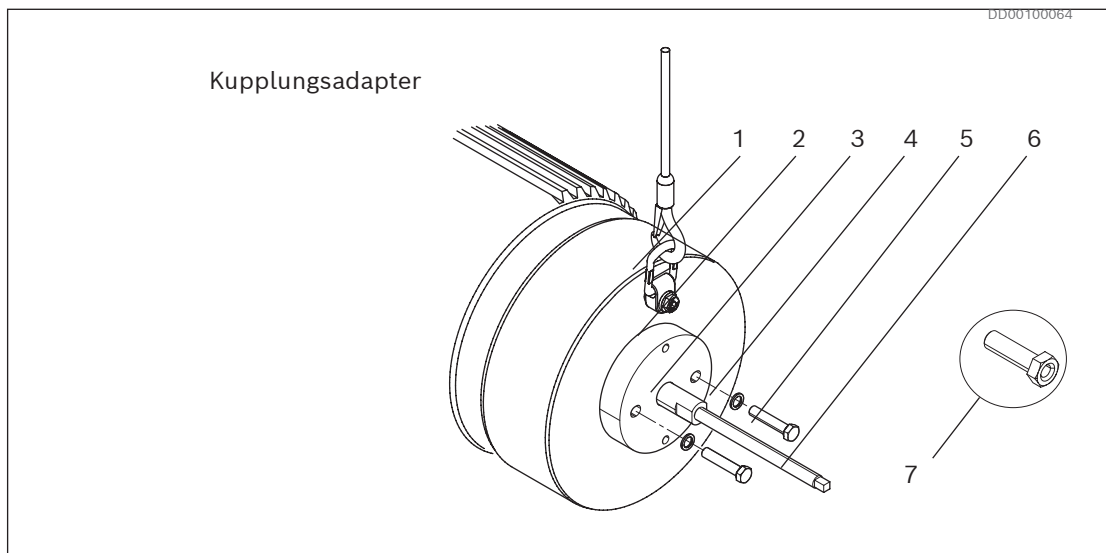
Montagewerkzeug zum Abbauen des Kupplungsadapters
